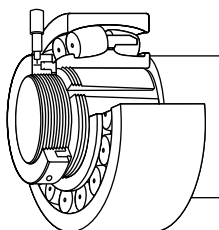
Piuliță hidraulică folosită la montarea rulmentului pe o bușă de extracție.
